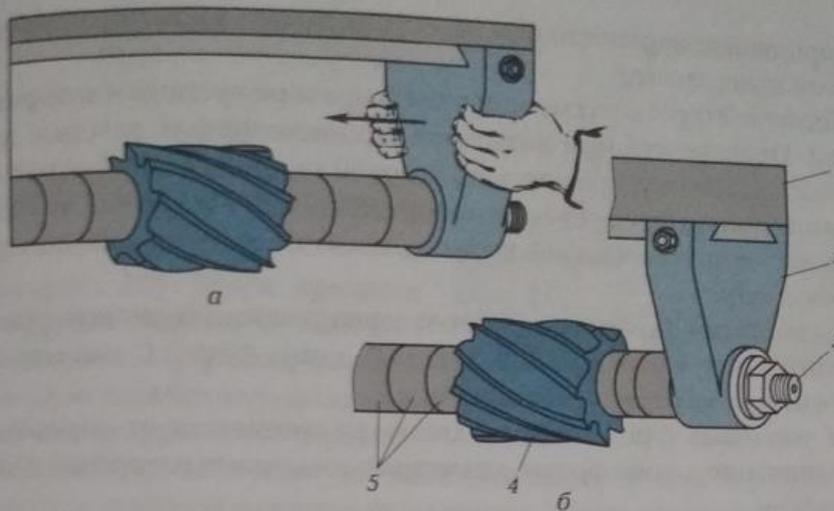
Установка оправки с цилиндрической фрезой на станок:
